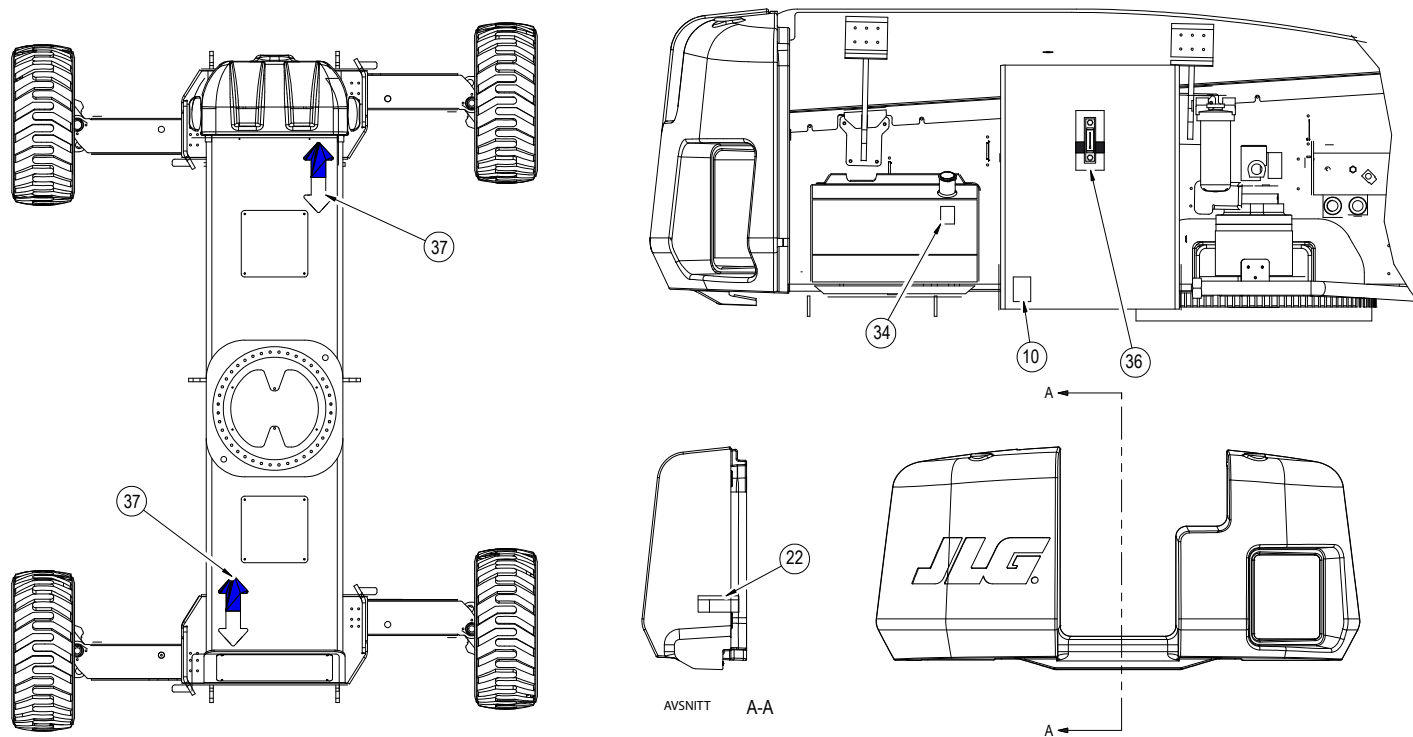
Dekalplacering - Serienummer 0300141446 till nu - Endast CE - Blad 2 av 5
